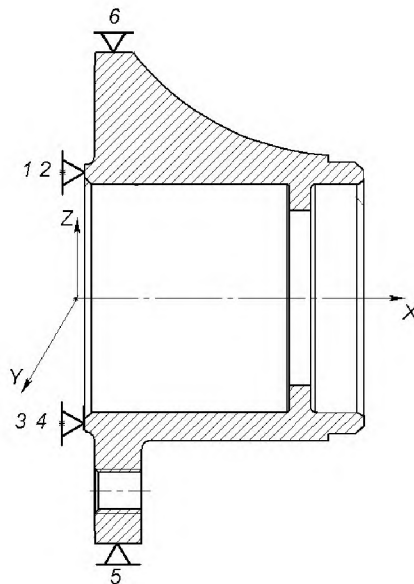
Теоретична схема базування заготовки при другій операції
